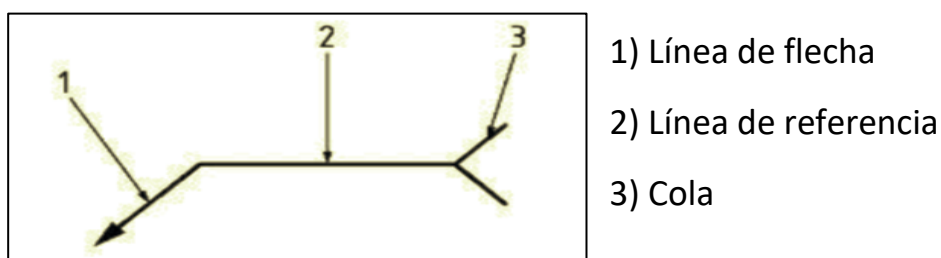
Símbolo de soldeo básico. Fuente: ISO 2553.
